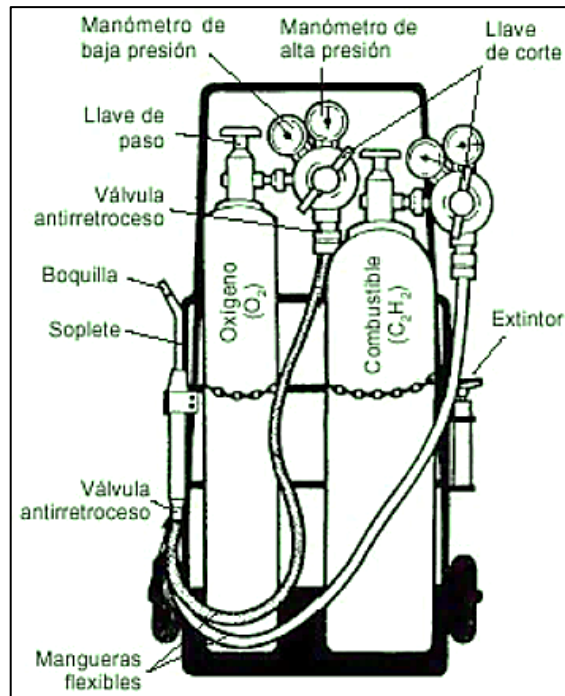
Equipo soldadura oxiacetilénica
